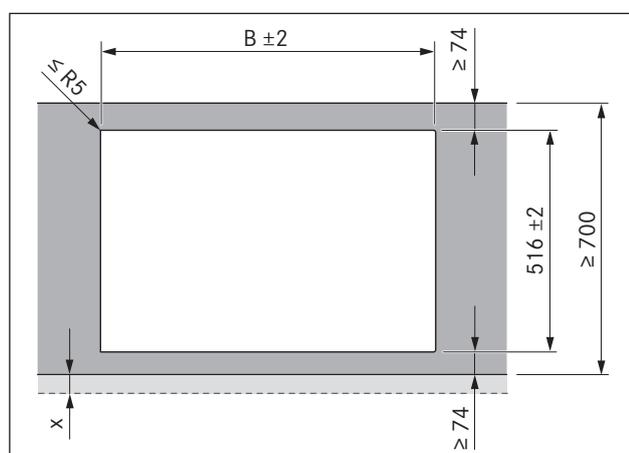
Medidas de recorte, montagem por sobreposição
